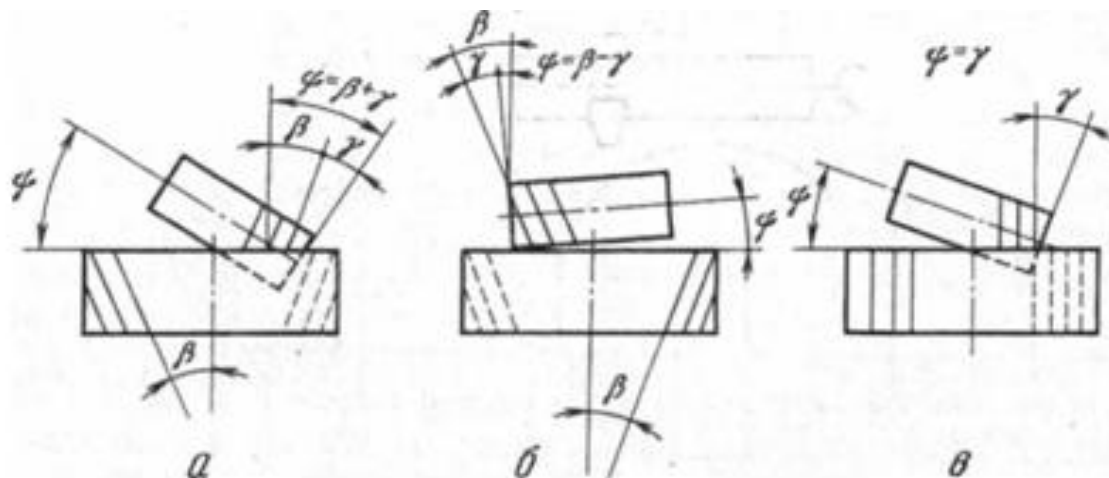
Установка шпинделя фрезы относительно нарезаемых цилиндрических колес: а – при разных направлениях винтовых линий на фрезе и на колесе, б – при одинаковых направлениях винтовых линий на фрезе и на колесе, г – прямозубых, γ – делительный угол подъема линии витка фрезы, ψ – угол наклона суппорта фрезы.
